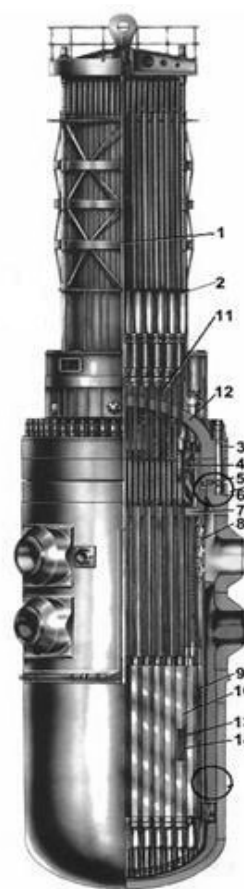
Реактор ВВЭР-1000 в сборе: 1 – верхний блок; 2 – привод СУЗ; 3 – шпилька; 4 – труба для загрузки образцов-свидетелей; 5 – уплотнение; 6 – корпус реактора; 7 – блок защитных труб; 8 – шахта; 10 – топливные сборки; 11 – теплоизоляция реактора; 12 – крышка реактора; 13 – регулирующие стержни; 14 – топливные стержни
